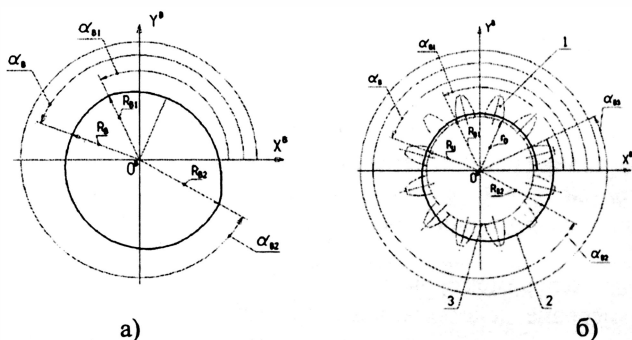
Контур, описываемый катающим радиусом валка (а); круглая шестерня с центроидой. 1 – шестерня; 2 – центроида шестерни; 3 – основная окружность шестерни (б)
